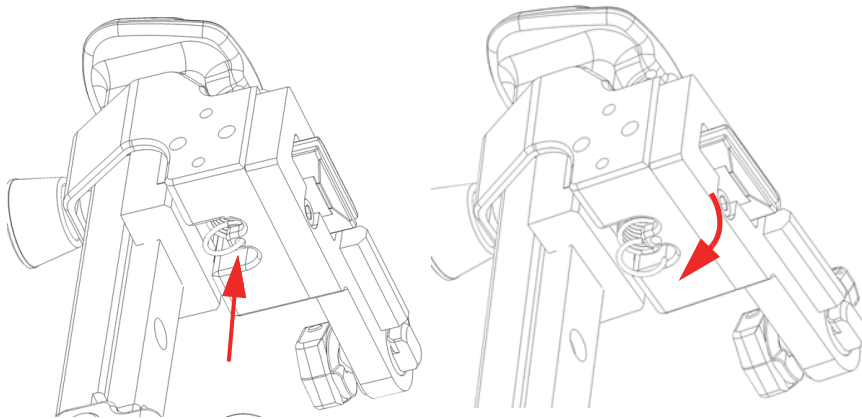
Sprungfeder aus der Bohrung entfernen
